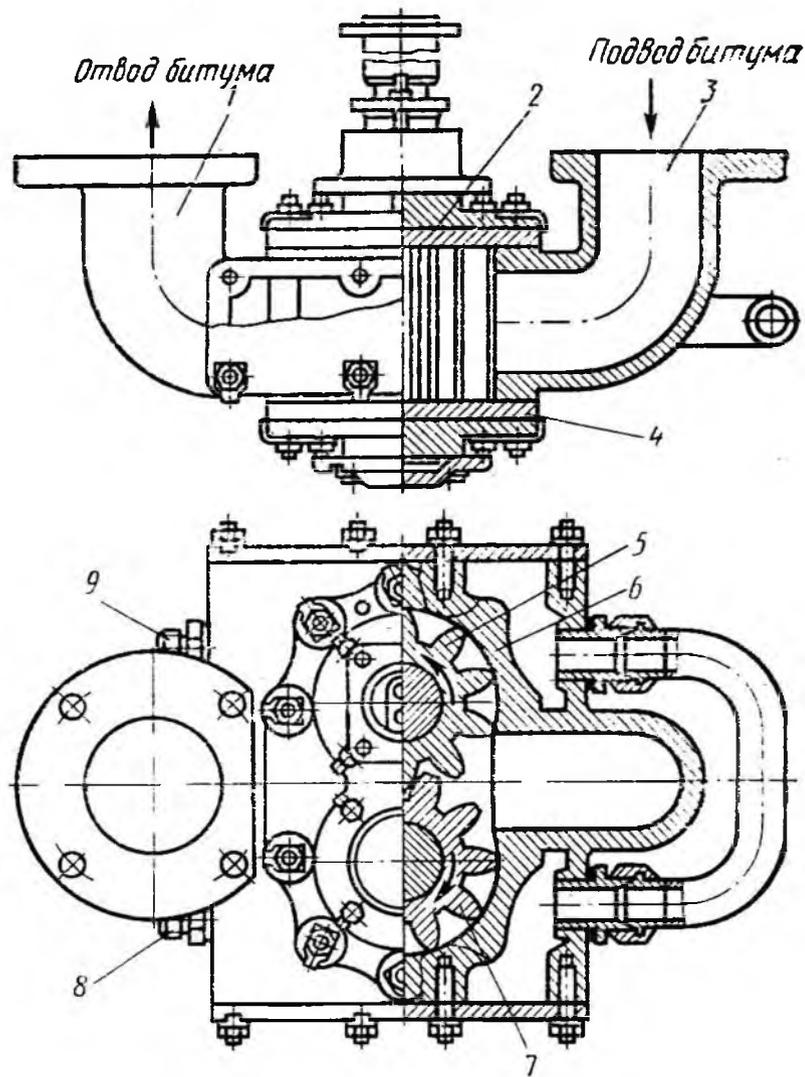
Погружаемый нагревательно-перекачивающий агрегат
